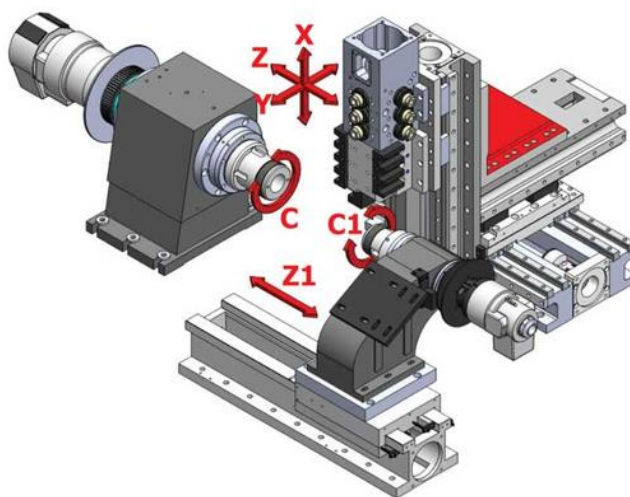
Схема токарного центра з проти шпинделем [1]
